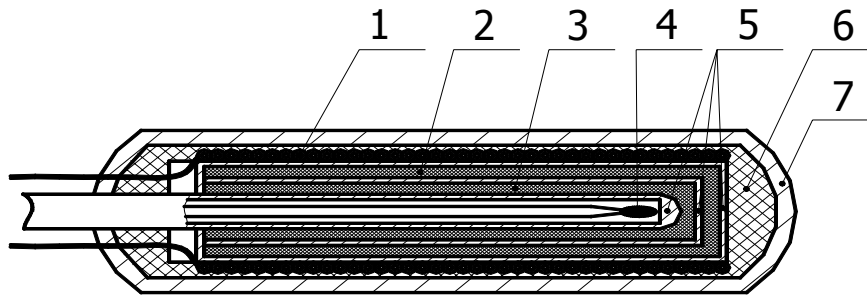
Самокалибрующийся датчик температуры (1 – управляемый нагревательный элемент; 2 и 3 – реперные металлы; 4 - первичный измерительный преобразователь (ПИП); 5 – тигли, выполненные из никеля; 6 - порошок окиси магния; 7 – металлический корпус)
